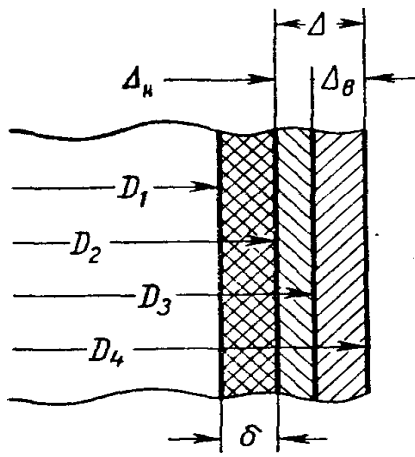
Схема розміщення припусків і допусків кувалдної поковки:
